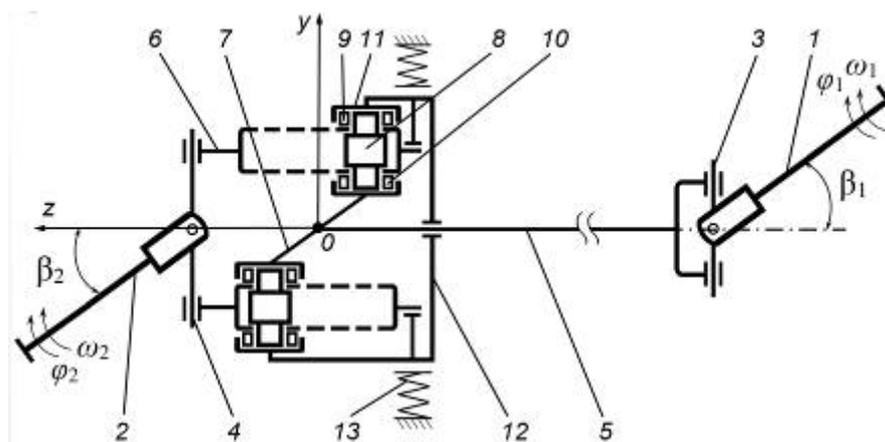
Кинематическая схема двухшарнирного приводного вала со встроенной ППТК
